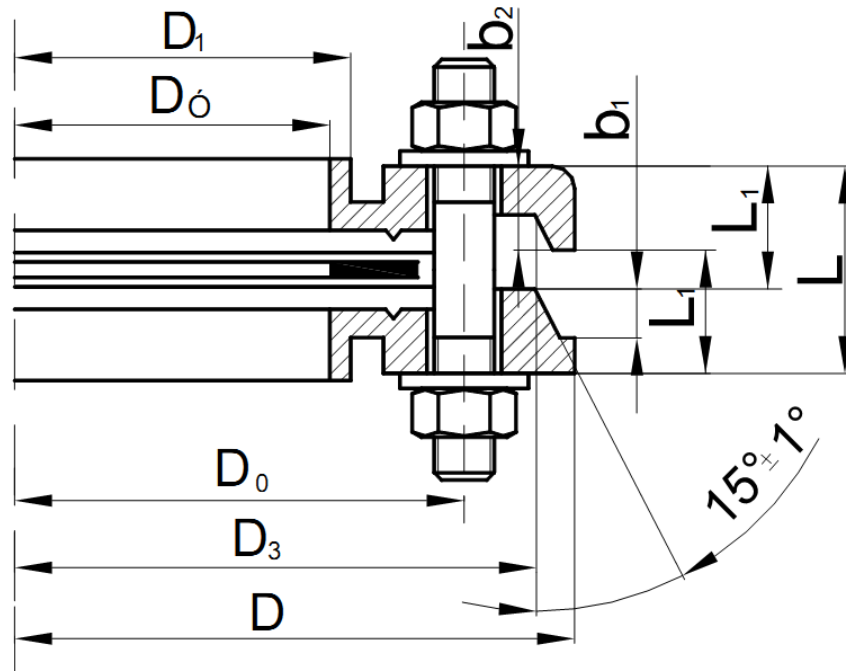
Соединение с плоской металлической прокладкой и канавочно-клиновым уплотняющим профилем
